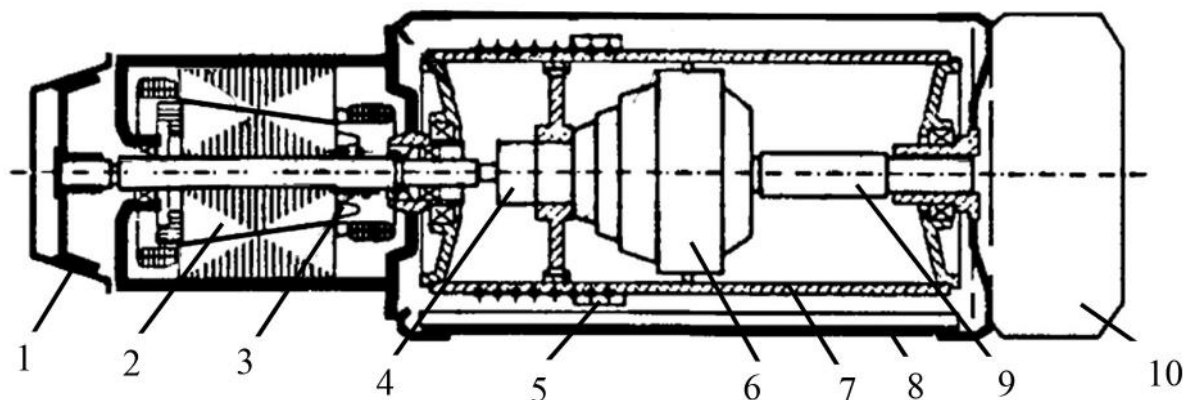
Механизм подъема тали серии М фирмы РОДЕМ: 1 – конический тормоз; 2 – конический ротор; 3 – тормозная пружина; 4 – муфта; 5 – канатоукладчик; 6 – трехступенчатый планетарный редуктор; 7 – канатный барабан; 8 – корпус; 9 – заторможенный вал; 10 – блок управления
